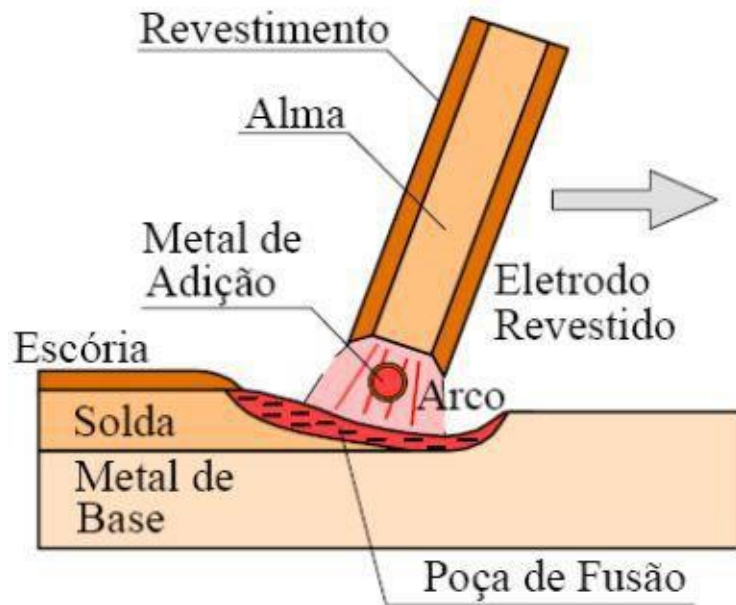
Esquema de soldagem SMAW (Adaptado de [20]).
